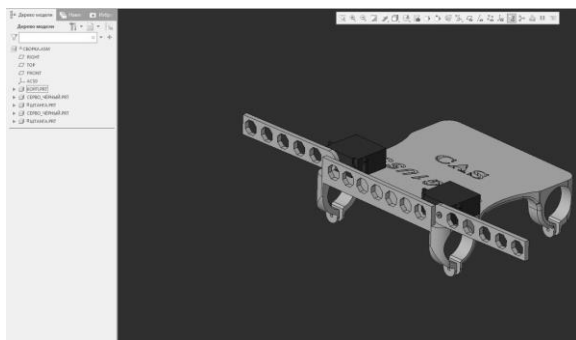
Сборка прототипа с раскрытыми штангами
